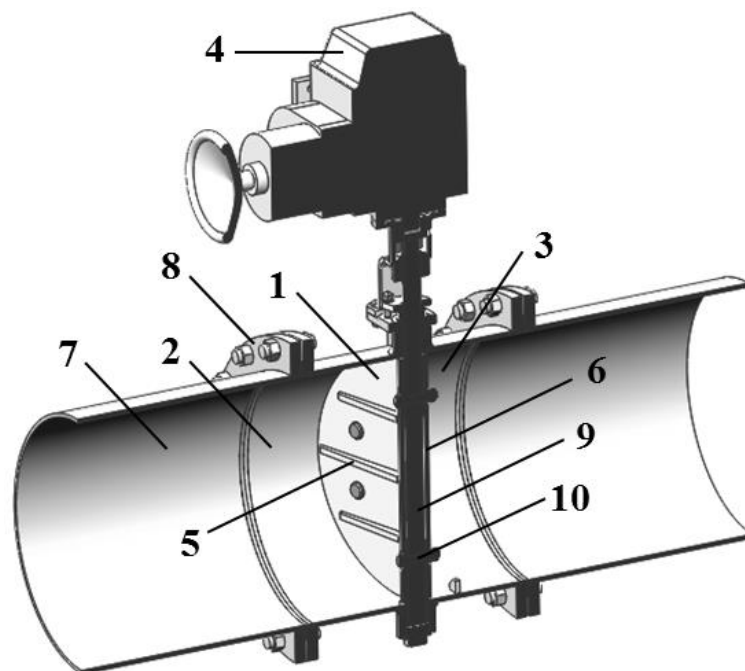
Затвор ДХО DN 400 PN 2,5 у з'єднанні з магістраллю: 1 – диск; 2 – вхідний патрубок; 3 – вихідний патрубок; 4 – МЕОФ (механізм однооборотного електричного фланцевого приводу); 5 – ребра жорсткості; 6 – дискова труба; 7 – магістраль; 8 – фланці; 9 – вал; 10 – болтове з'єднання
